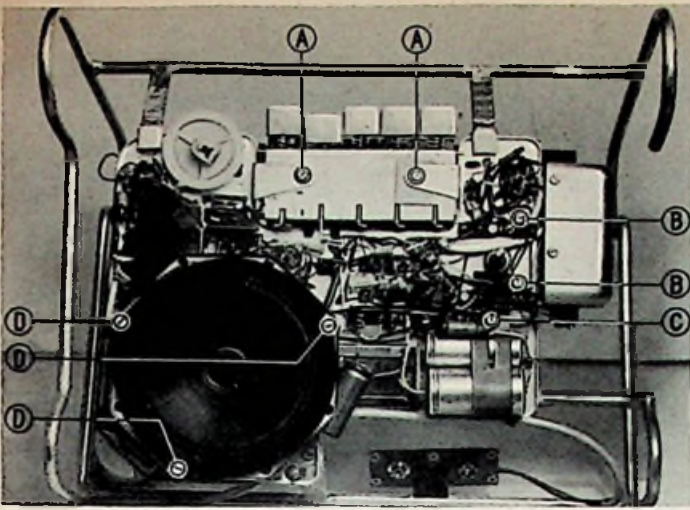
Vorderansicht des Chassis des Philips-Reiseosupers Georgette. Die mit Kreisen gekennzeichneten Schrauben dienen zur Befestigung leicht austauschbarer Einheiten; A = Befestigungsschrauben für Tastatur, B = Befestigungsschrauben für UKW-Einheit, C = Befestigungsschrauben für Elektrolytkondensatoren, D = Schrauben für Lautsprecher
